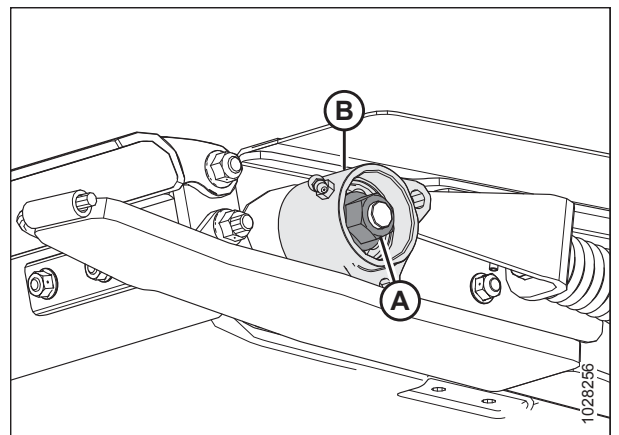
Rodamiento de rodillo tensor: lado izquierdo
